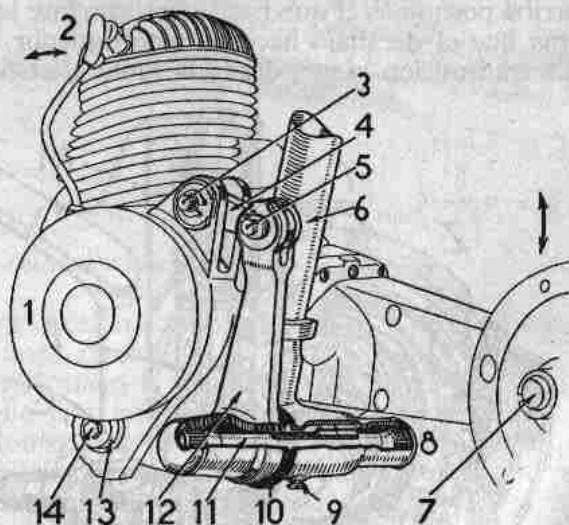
Suspensión *Lambretta* por barra de torsión.
